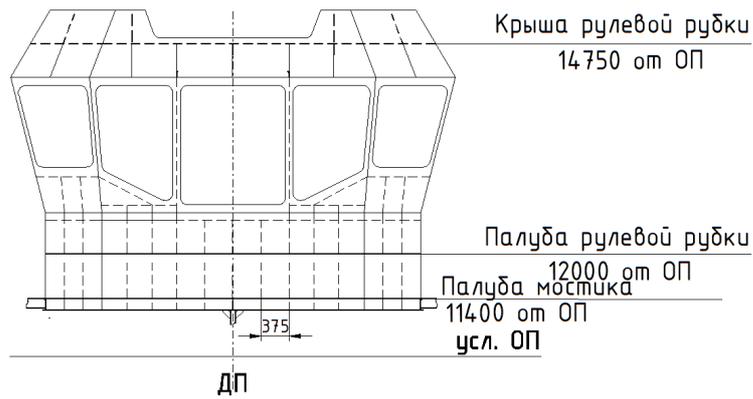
Конструктивный чертеж носовой стенки рулевой рубки.
